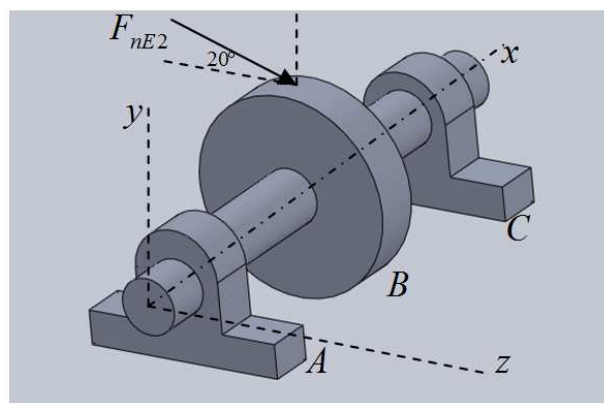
Disposición del engrane 2 sobre el eje 2.
